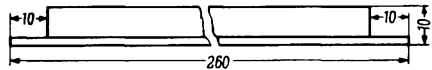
Winkel für die Oberkante der Frontplatte (Winkel-Aluminium 10 × 10 × 2 mm). Maßstab 1 : 2
